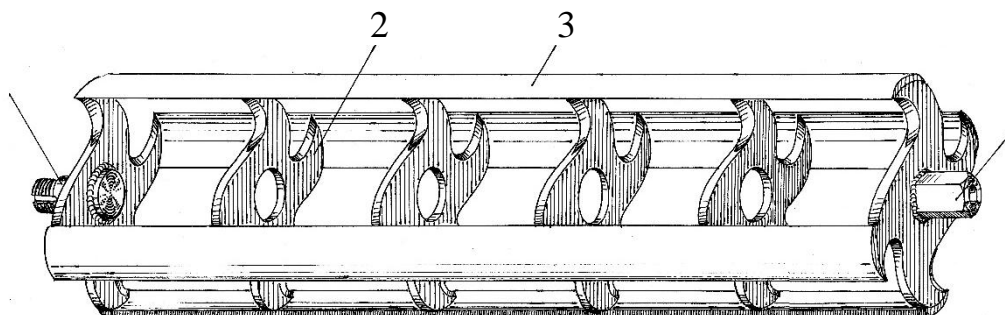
Фрезерный рабочий орган «безвального типа»:
